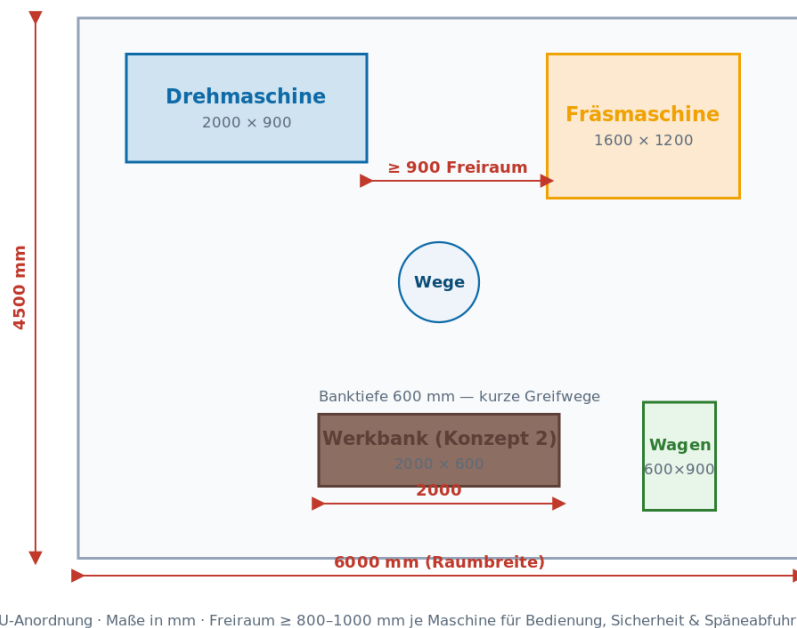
Maßstäblicher Werkstatt-Grundriss
